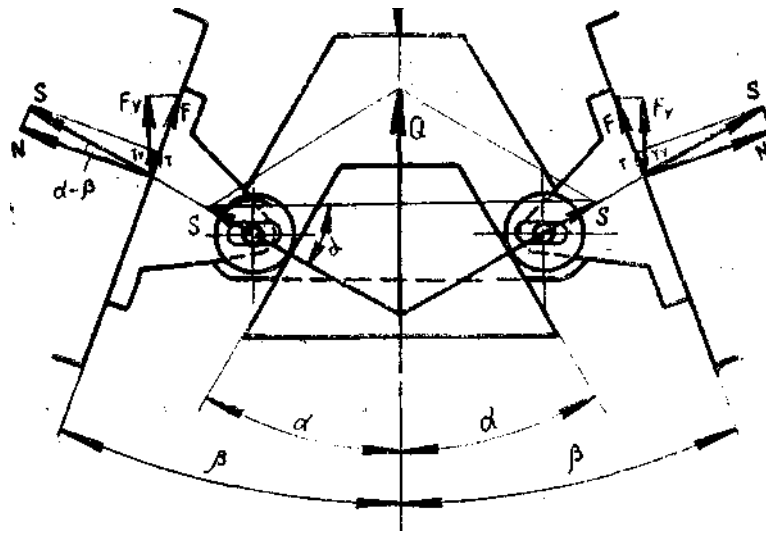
Розрахункова схема фрикційної виливниці
